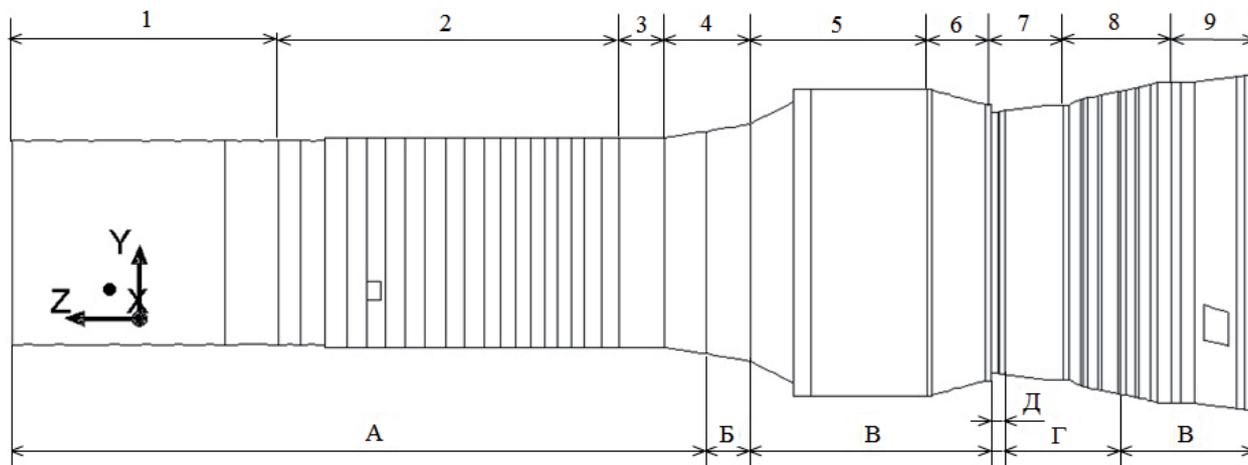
Характерные участки корпуса ГТД: 1 — проставка; 2 — корпус компрессора низкого давления (КНД); 3 — переходник; 4 — силовой корпус КВД; 5 — кожух камеры сгорания (КС); 6 — силовой корпус турбины высокого давления (ТВД) и турбины низкого давления (ТНД); 7 — опорный венец (ОВ) ТНД; 8 — корпус силовой турбины (СТ); 9 — ОВ СТ; А — металлический корпус ГТД без изоляции; Б — мат МБПОР-5 толщиной 5 мм; В — мат АТМ-10К толщиной 20 мм; Г — мат МТПБа-КТ-6 толщиной 30 мм; Д — мат МТПБа-КТ-6 толщиной 40 мм
